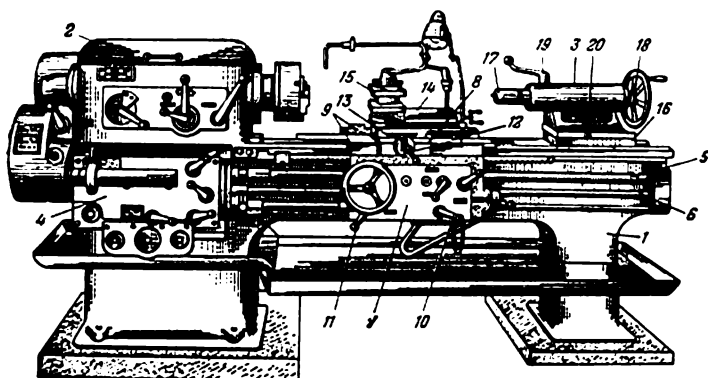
Vue d'ensemble d'un tour à chariotier modèle 1A62
